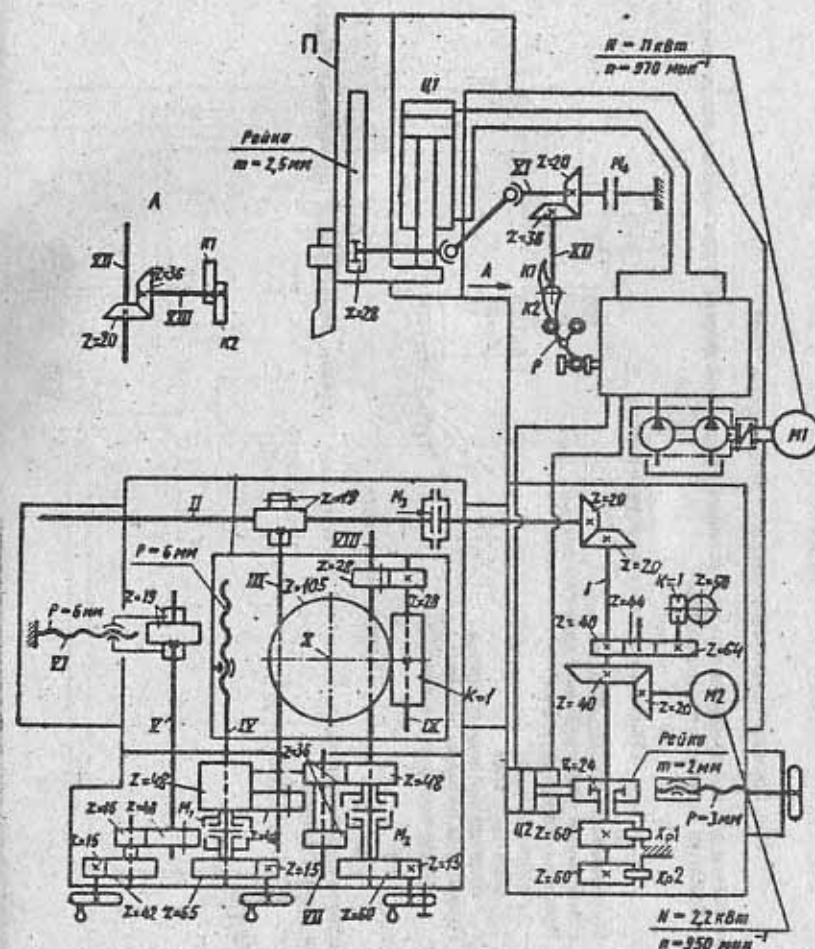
Кинематическая схема долбежного станка мод. 7Д430
